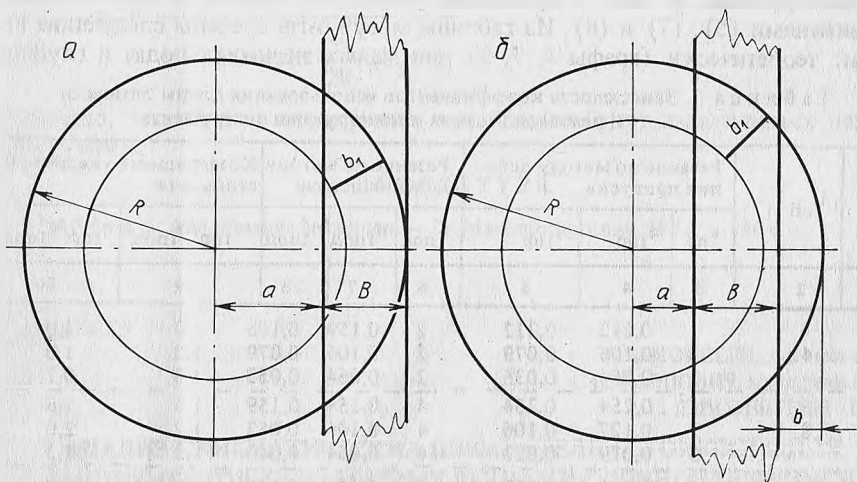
Схема торцевого фрезерования при $B < D$ и при разном расположении детали относительно фрезы (а) и (б)
